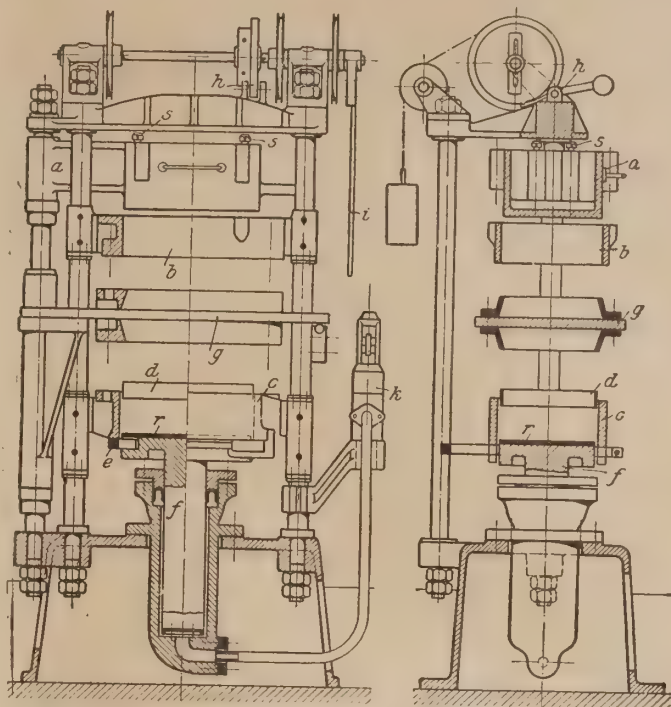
u. 8. Hydraulische Formmaschine mit Füllring und Gegenpreßanschlag
